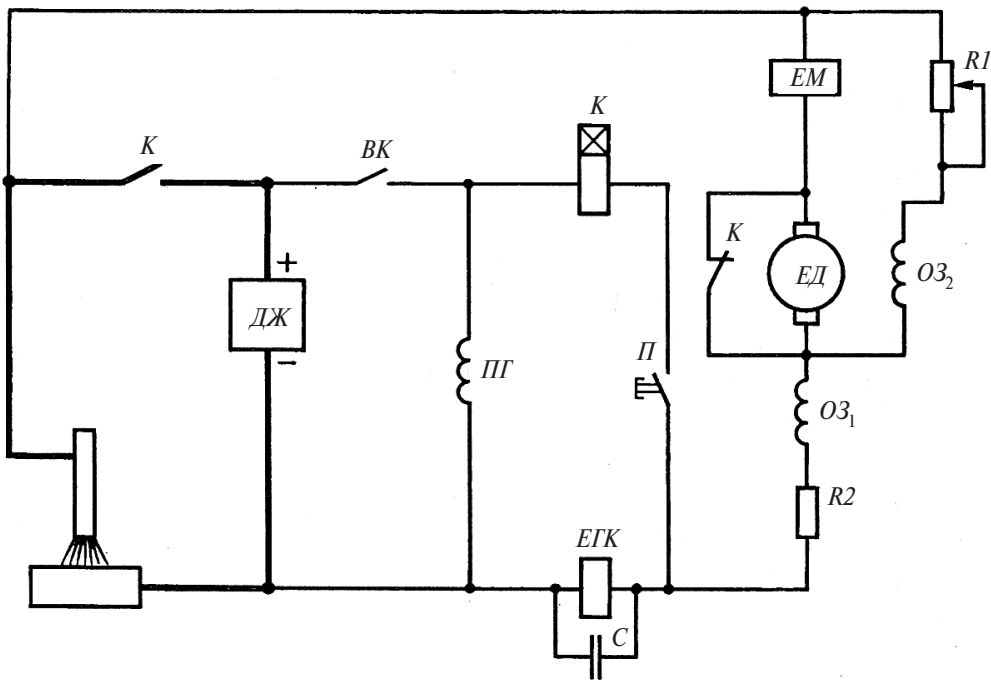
Монтажна схема установки для напівавтоматичного зварювання плавким електродом у середовищі захисного газу:
